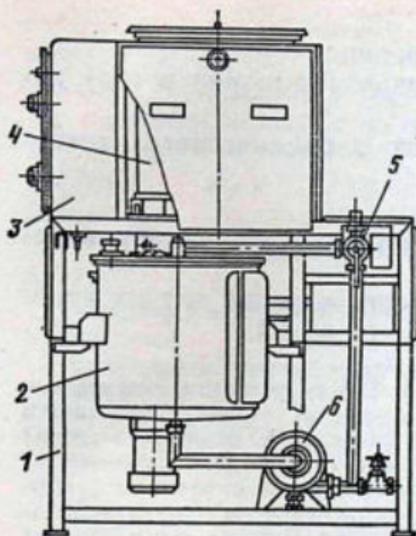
Автоматизированная установка для приготовления жидких питательных смесей УПМ-1000:
